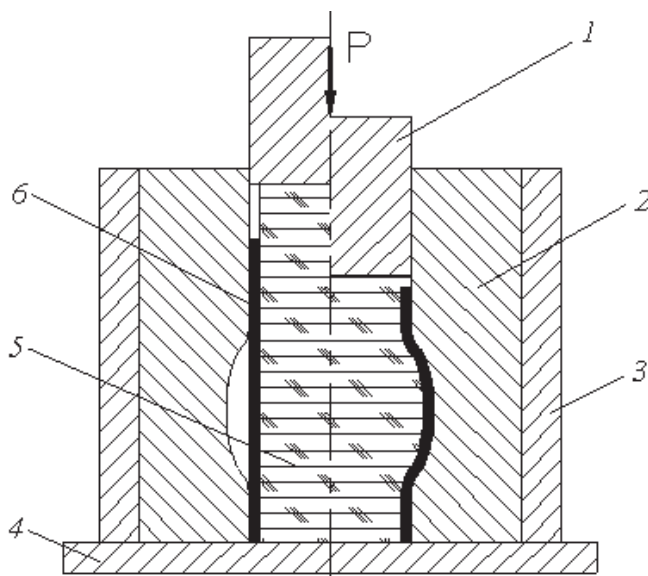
Штамп для раздачи трубчатой заготовки с использованием стержня из льда или снега
